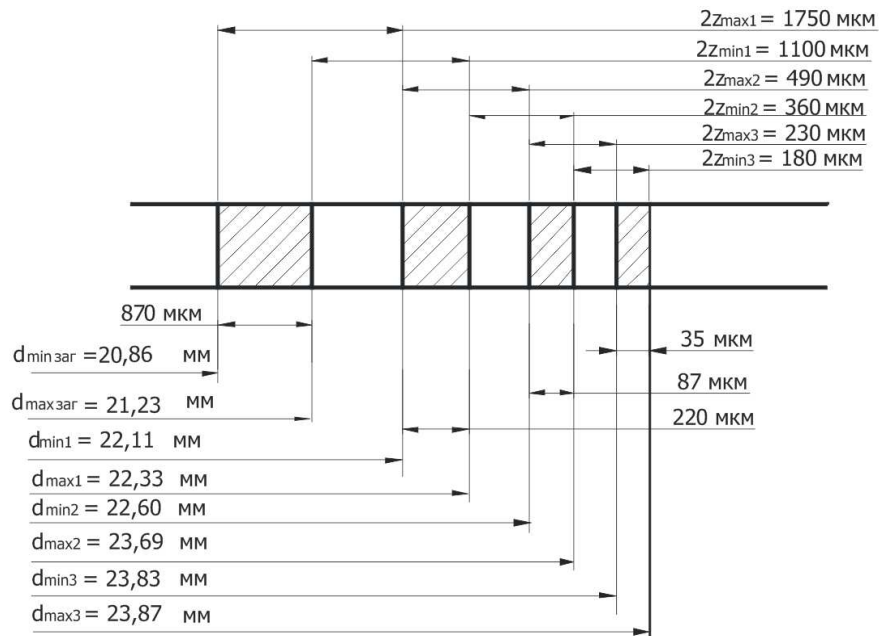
Схема графічного розміщення припусків і допусків напорного диска на поверхню $\varnothing 22 \text{ H7}$.
